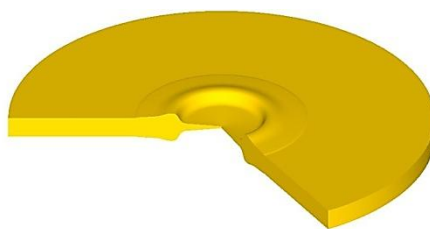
Здеформована заготовка з перемичкою в розрізі після видавлювання
